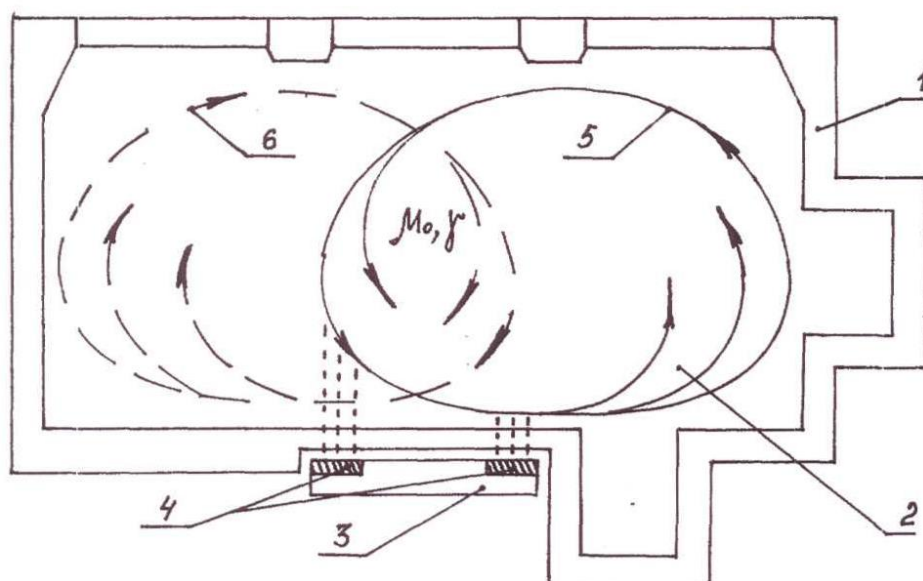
Индуктор МГД-перемешивателя, установленный с боковой стороны ванны
